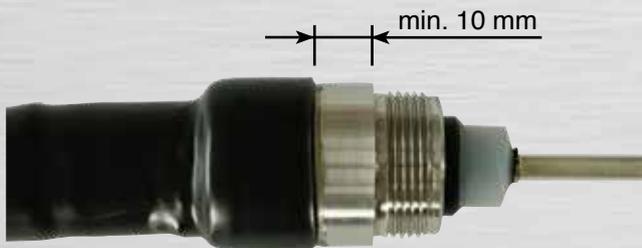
Abstand des Schrumpfschlauches zum Gewinde
